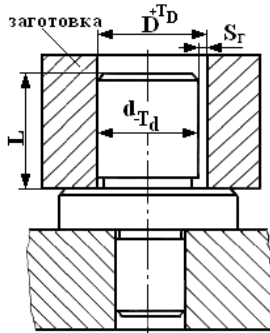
Схема базирования заготовки на цилиндрический палец
